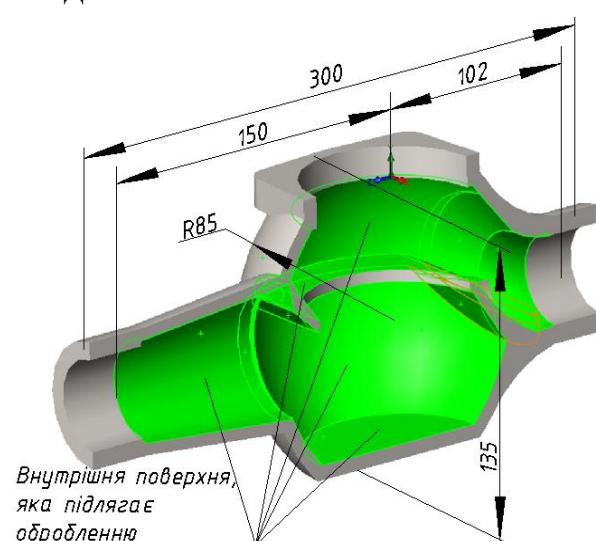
Загальний вигляд корпусу водолічильника КВБ-10 з виділеною внутрішньою поверхнею, що підлягає обробленню (переріз)
